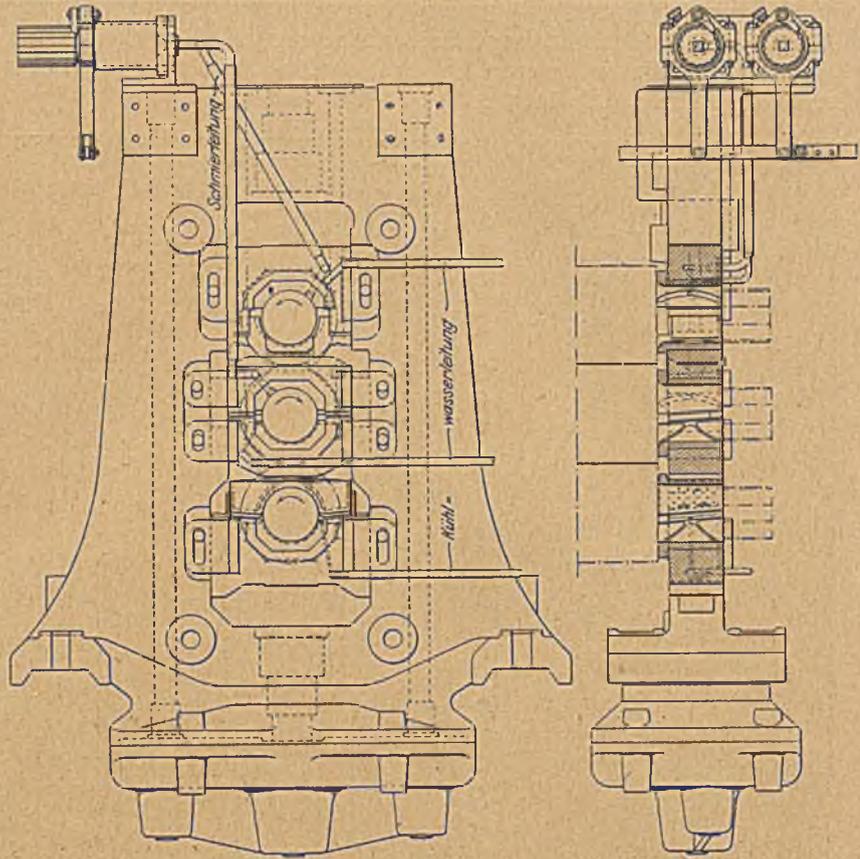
Walzgerüst einer Feinstrabe mit Schmiervorrichtung.
